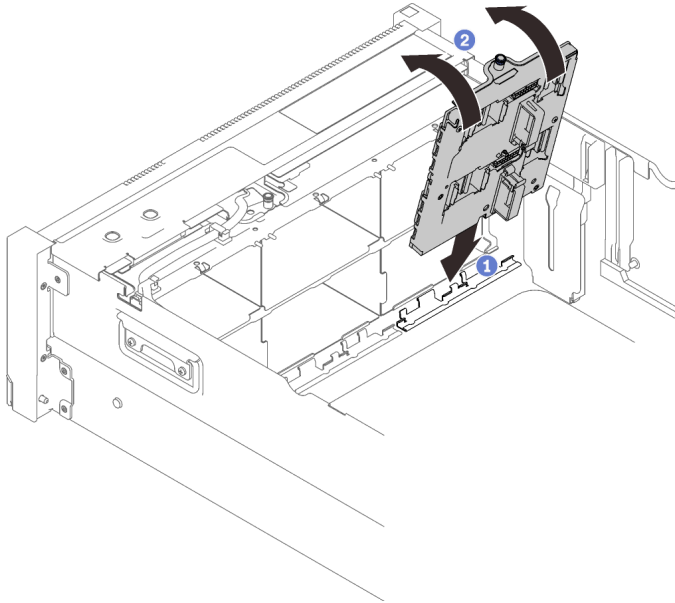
Instalando o conjunto de portadora do backplane de unidade
